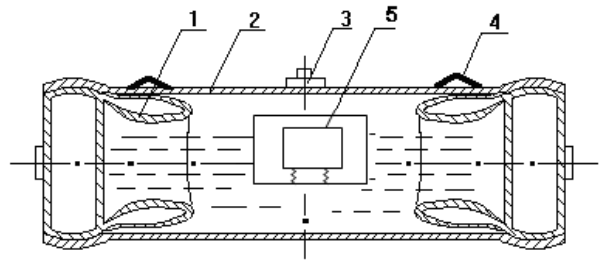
Схема резервуара з плаваючим в контейнері зразком озброєння на пружній основі (1 – допоміжні рукава; 2 – корпус резервуара; 3 – зливо-наливне пристосування; 4 – кріплення для переміщення резервуара; 5 – елемент озброєння)
